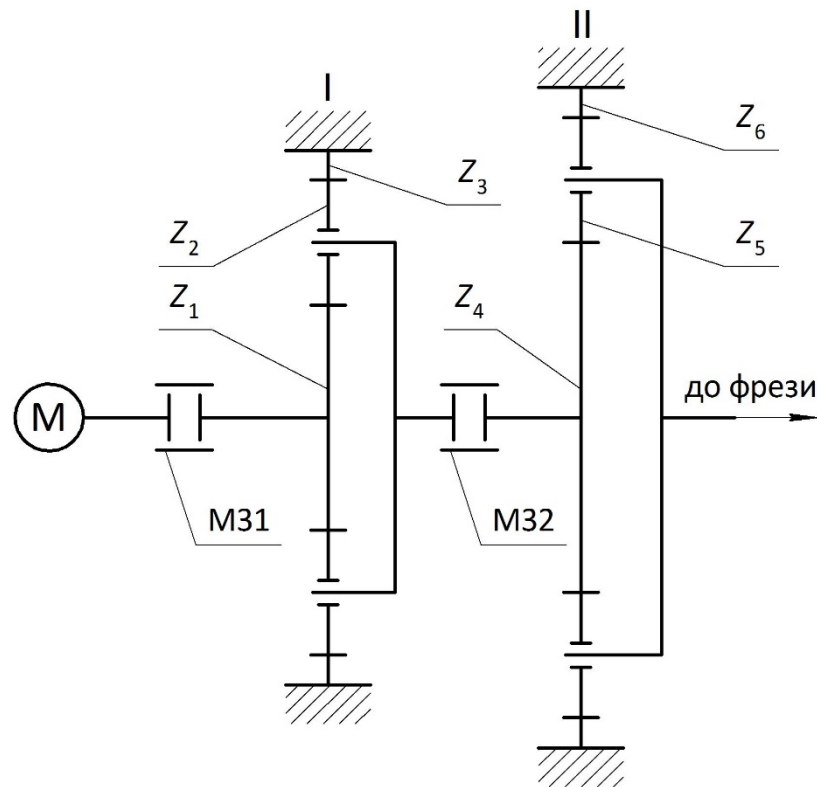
Кінематична схема редуктора приводу фрезерної головки: I та II ступені планетарних передач; М31, М32 – зубчасті муфти
